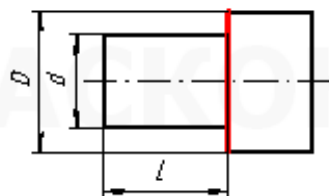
КТЭ торец открытый наружный для поверхностей №24,27,29,30
